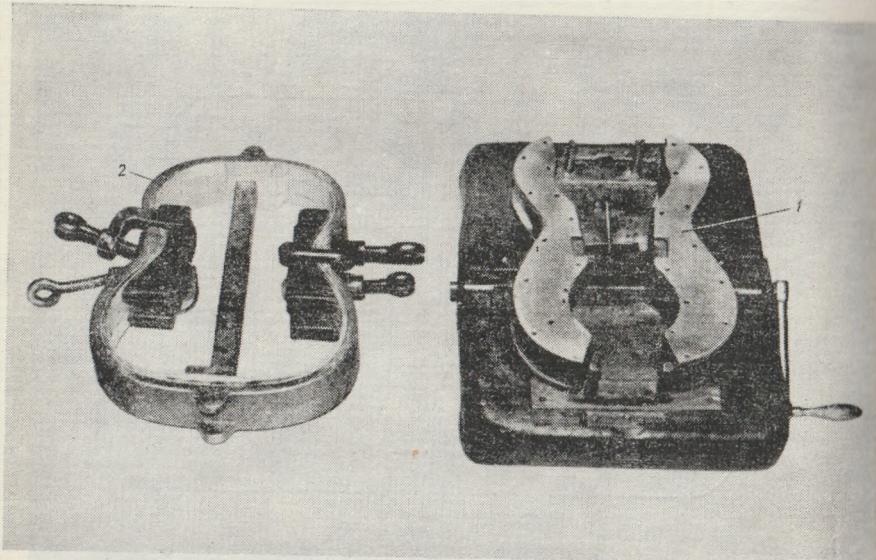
Собранный рамка корпуса гитары в шаблоне:
